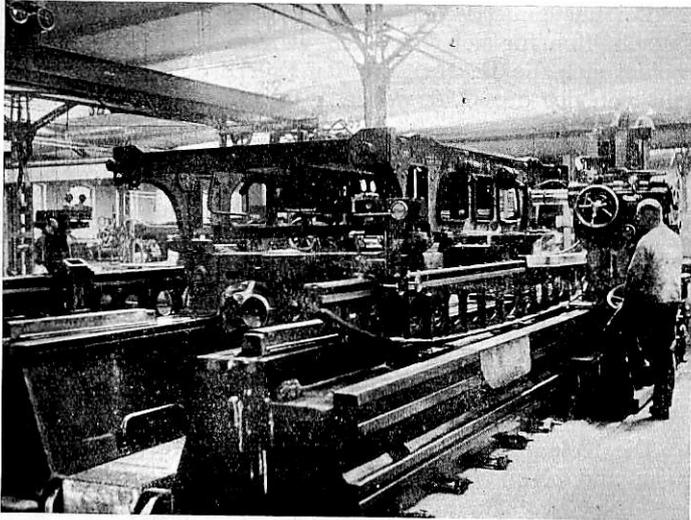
Meß- und Bearbeitungsmaschine für Drehgestelle.
